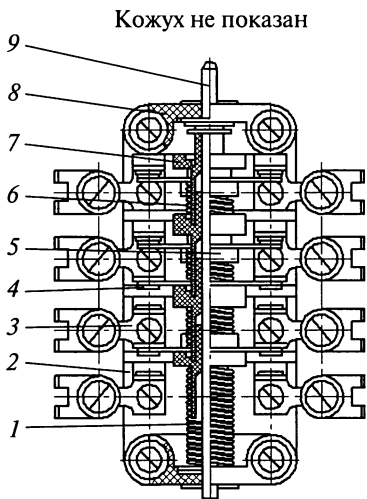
Блокировка электрическая низковольтная (без кожуха): 1 — отключающая пружина; 2 — панель изоляционная; 3 — контакт неподвижный; 4 — контакт подвижный; 5 — втулка; 6 — контактная пружина; 7 — втулка; 8 — стойка; 9 — шток
